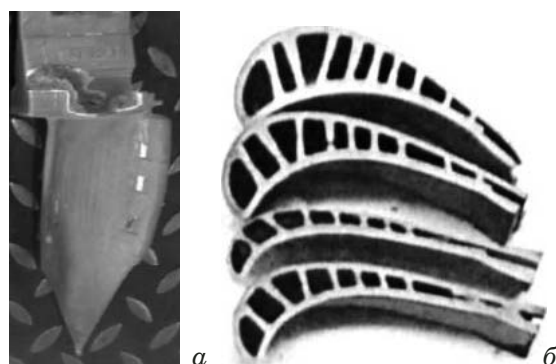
Отливка рабочей лопатки (а), макрошлифы поперечного сечения профиля пера лопатки после удаления стержня (б)
